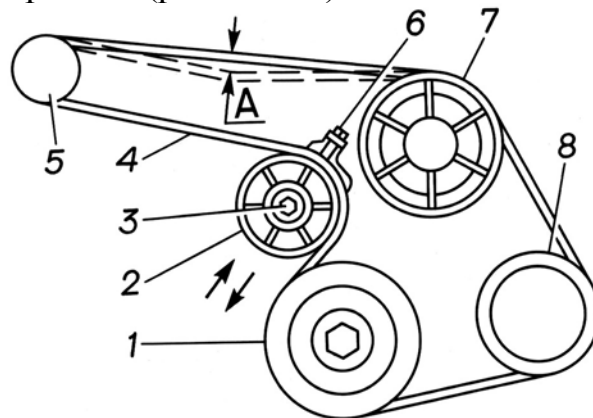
Схема натяжения ремня привода агрегатов: $A=14$ мм; 1 - шкив коленчатого вала; 2 - натяжной ролик; 3 - болт крепления натяжного ролика; 4 - поликлиновое ремни; 5 - шкив генератора; 6 - болт перемещения натяжного ролика; 7 - шкив водяного насоса; 8 - шкив насоса ГУР
